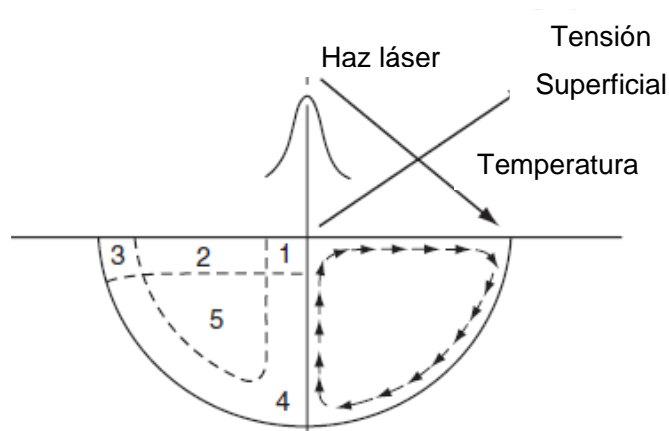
Esquema del efecto de la convección sobre la configuración del charco de soldadura en la soldadura láser en modo de conducción. [39]
